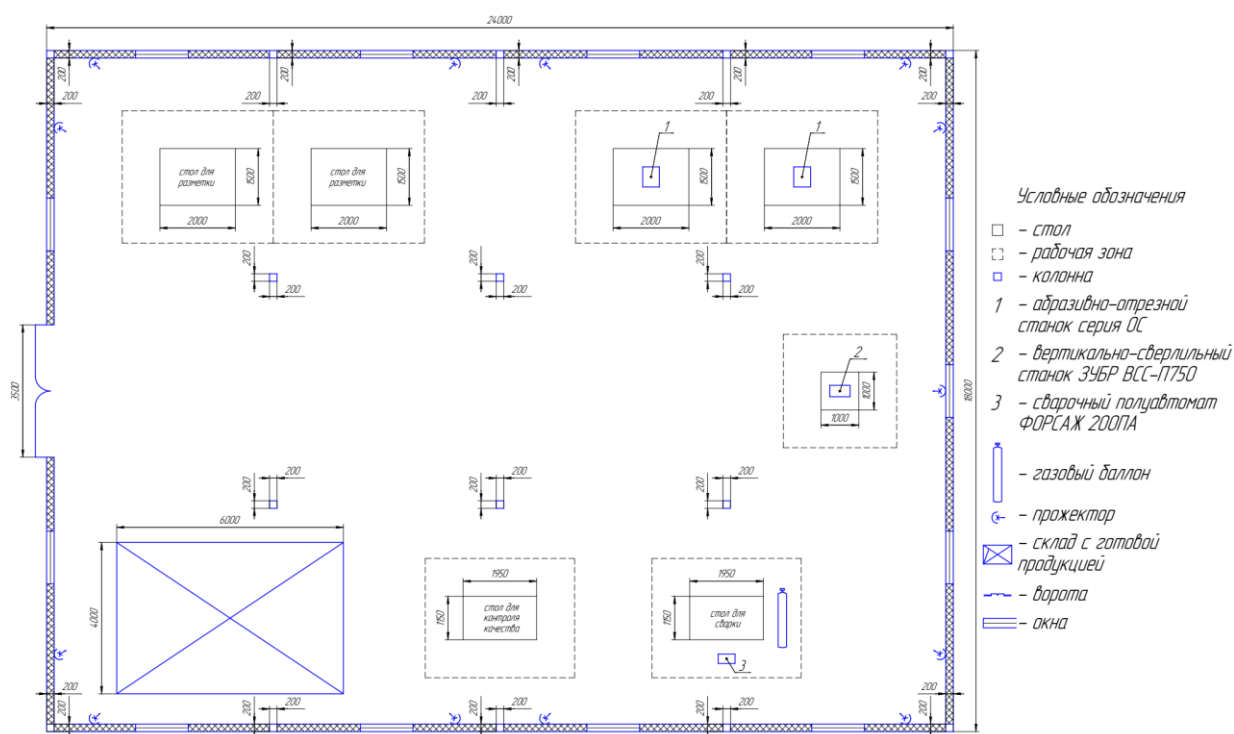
Планировка участка сборки и сварки стойки для штанги
